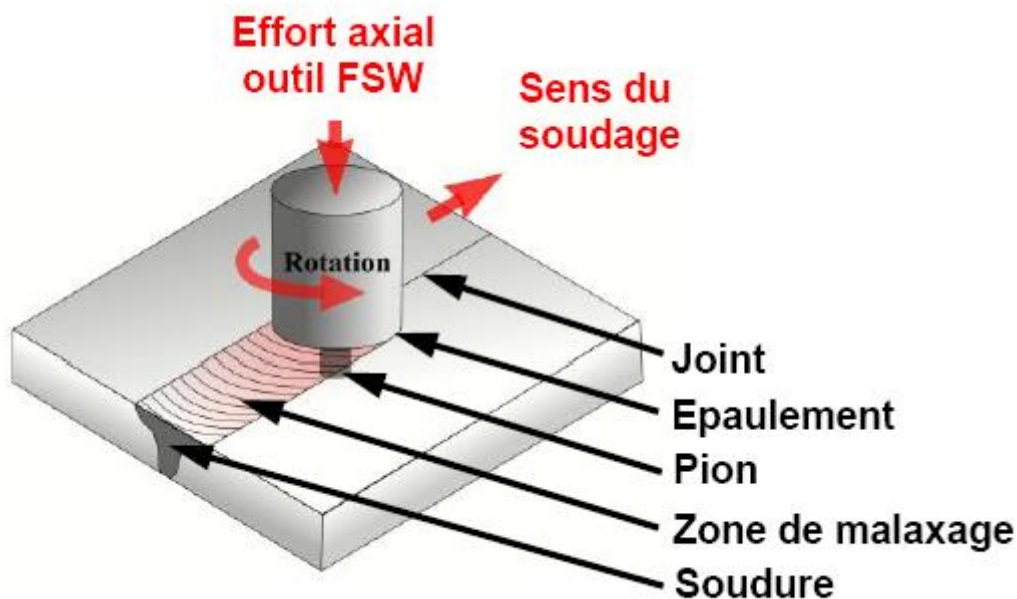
Illustration du principe de soudage par friction malaxage
